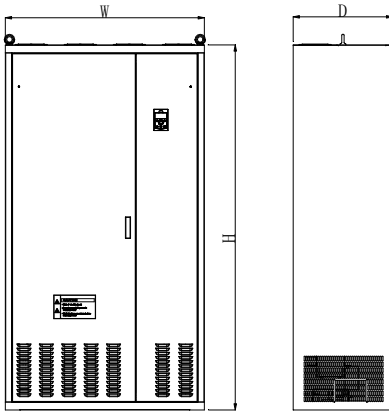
380V (4T) 450~800kW 变频器外型尺寸及安装尺寸示意图
